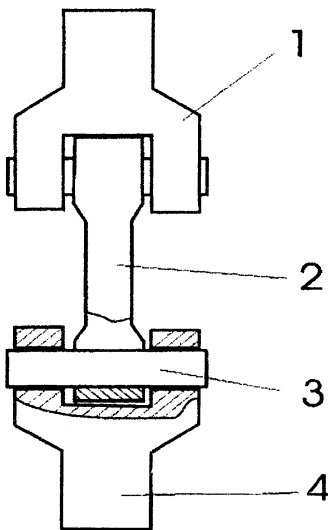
Схема испытания звена цепи на растяжение: 1 - верхний держатель, 2 - звено цепи, 3 - стержень, 4 - нижний держатель
